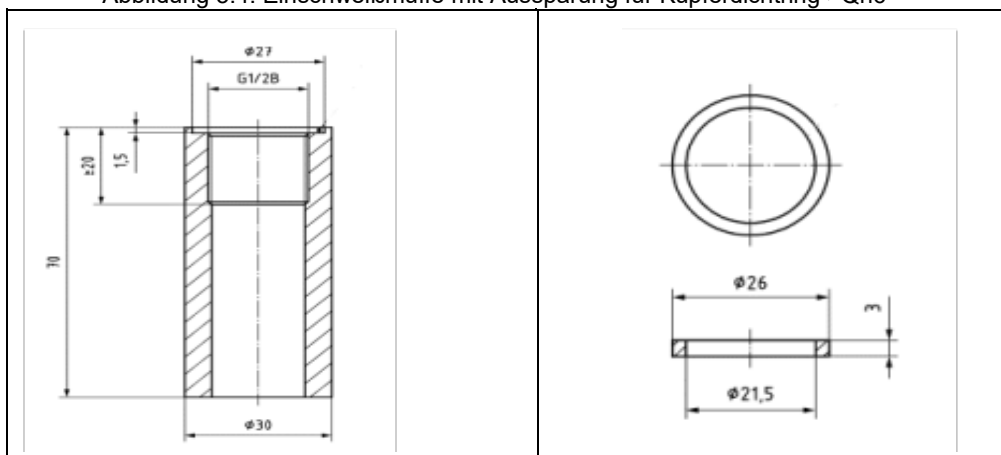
Einschweißmuffe mit Aussparung für Kupferdichtring >Qn6
